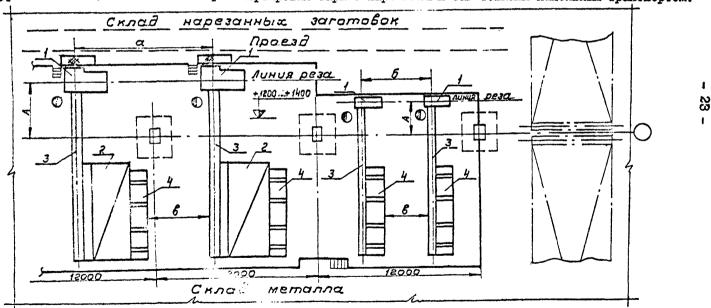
Рис. I. Схема расположения кривошиных ножения в 2-х парадлельных пролетах: I - пресс-ножницы; 2 - печь; 3 - рольгатр: 4 - стедлаж.
